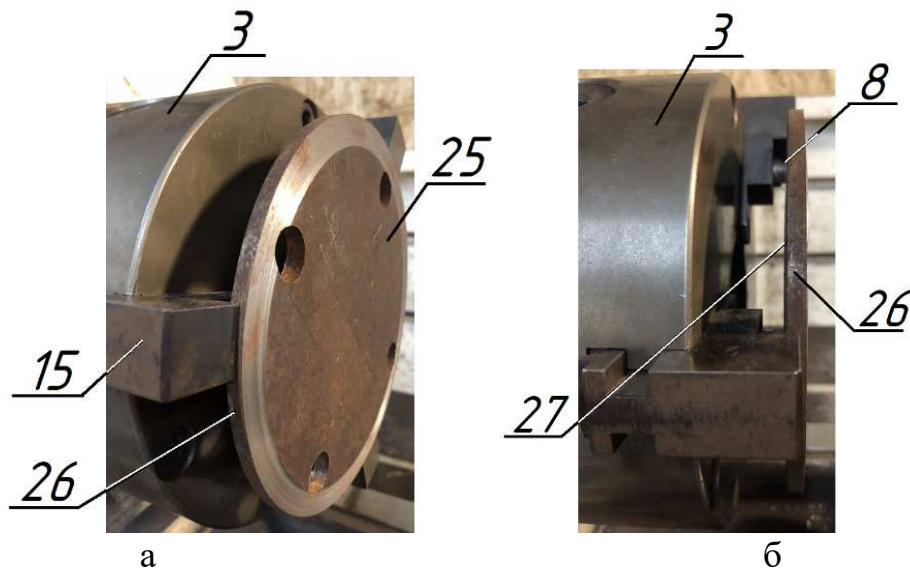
Заготовка «Диск» в обратных кулачках – а; заготовка «Диск» с упором в резьбовые шпильки – б.
